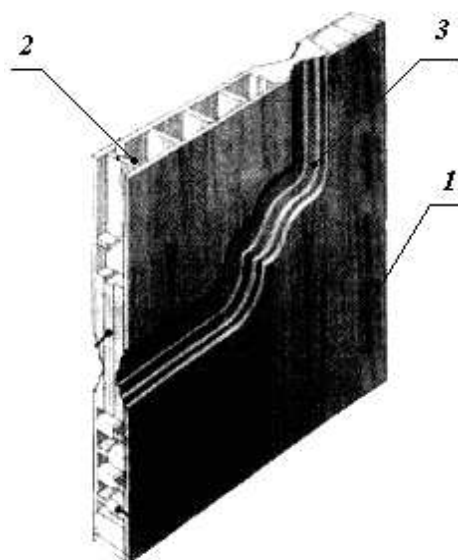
Дверь комбинированной конструкции: 1 – комбинированная коробка из клееного бруса, сотового наполнителя и облицовки (обшивки); 2 – объемная филленка с сотовым наполнением из МДФ; 3 – фигурная вставка-соединитель из массива древесины
